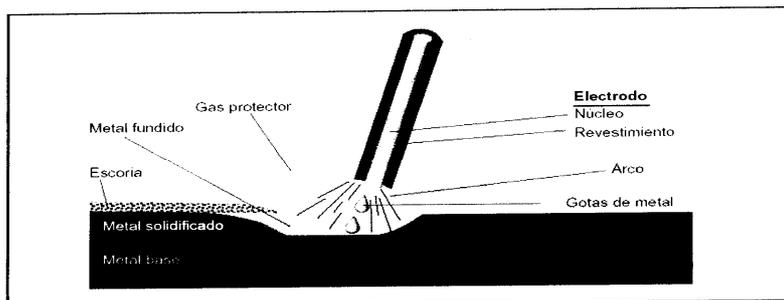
Proceso del sistema de soldadura de arco manual
